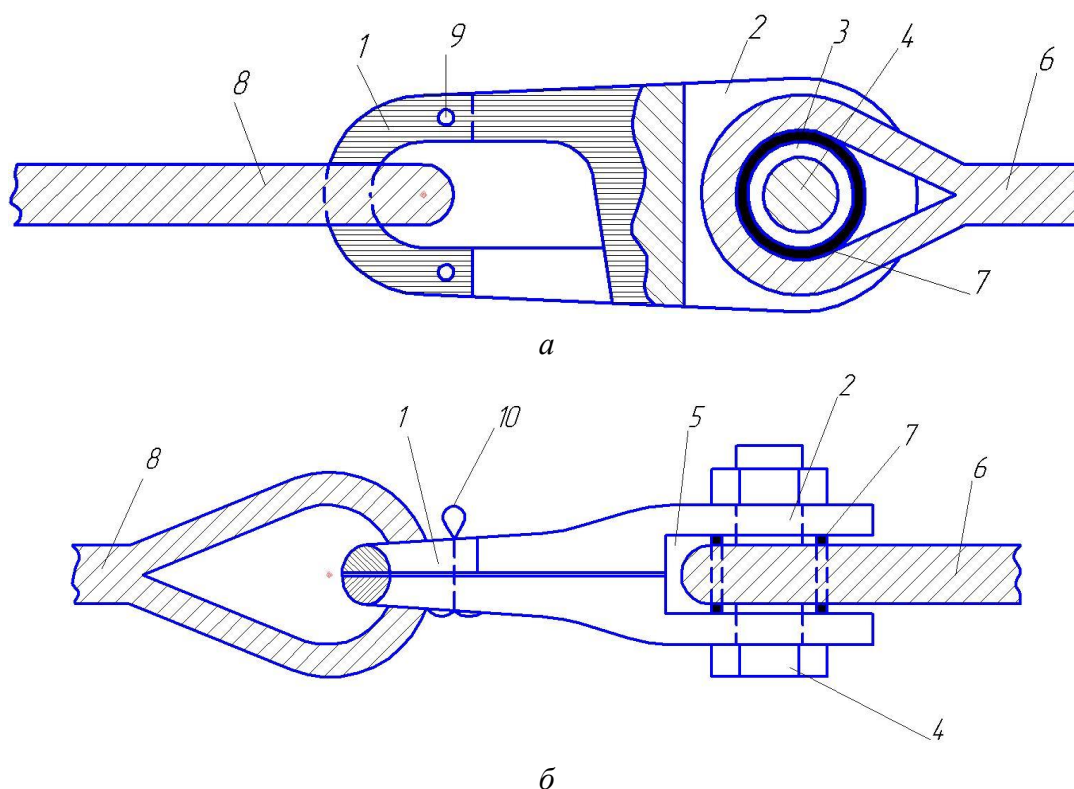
Устройство для соединения кантов: *а* – устройство, местный разрез на виде сбоку; *б* – тоже, вид сверху с сечением крюков
